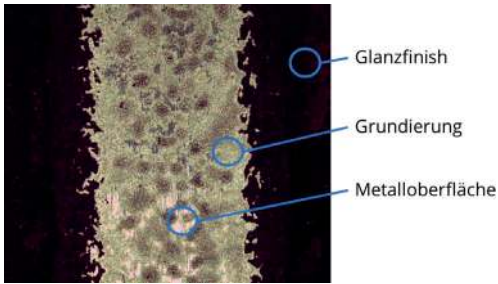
Partielle Schichtabtragung von einer PU-Lackschicht mit Grundierung von einem Aluminiumbauteil
